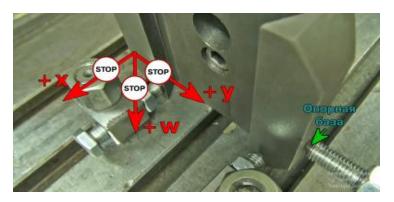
Для создания детали неподвижной, нужно дополнить опорную базу
